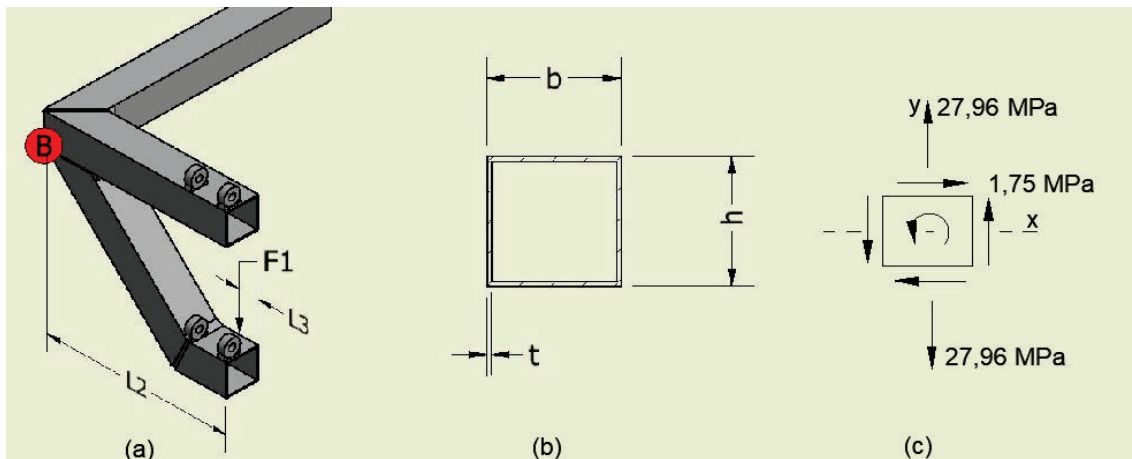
(a) Punto crítico en soldadura (b) Sección transversal del tubo y dimensiones (c) Elemento de esfuerzos en el punto B.
